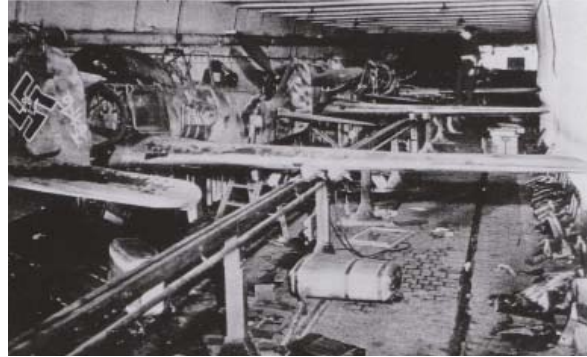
Tunnel de production d'avions pendant la guerre, 1945.
